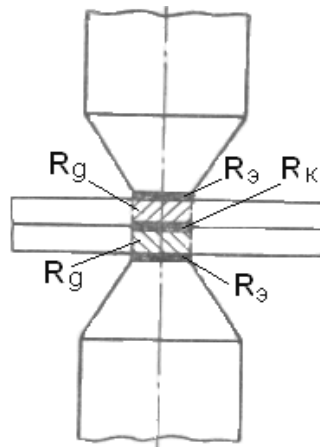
Сопротивление зоны сварки
